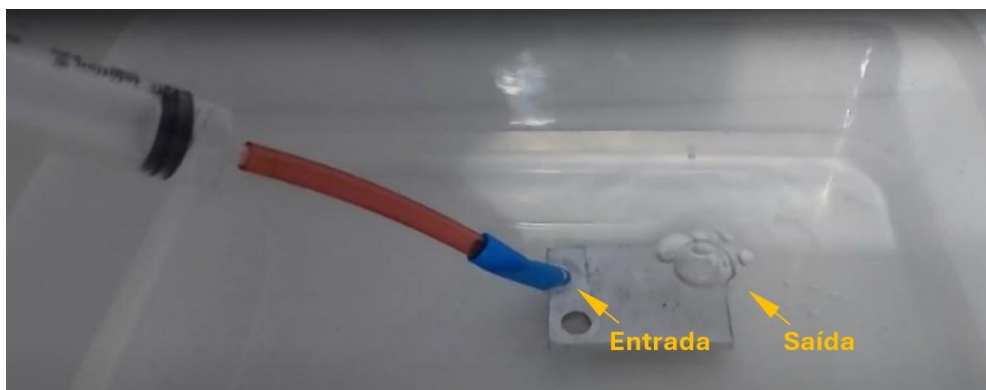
Teste de continuidade utilizando injeção de ar em canal de 0,5 mm. (Link para [vídeo](#)).
